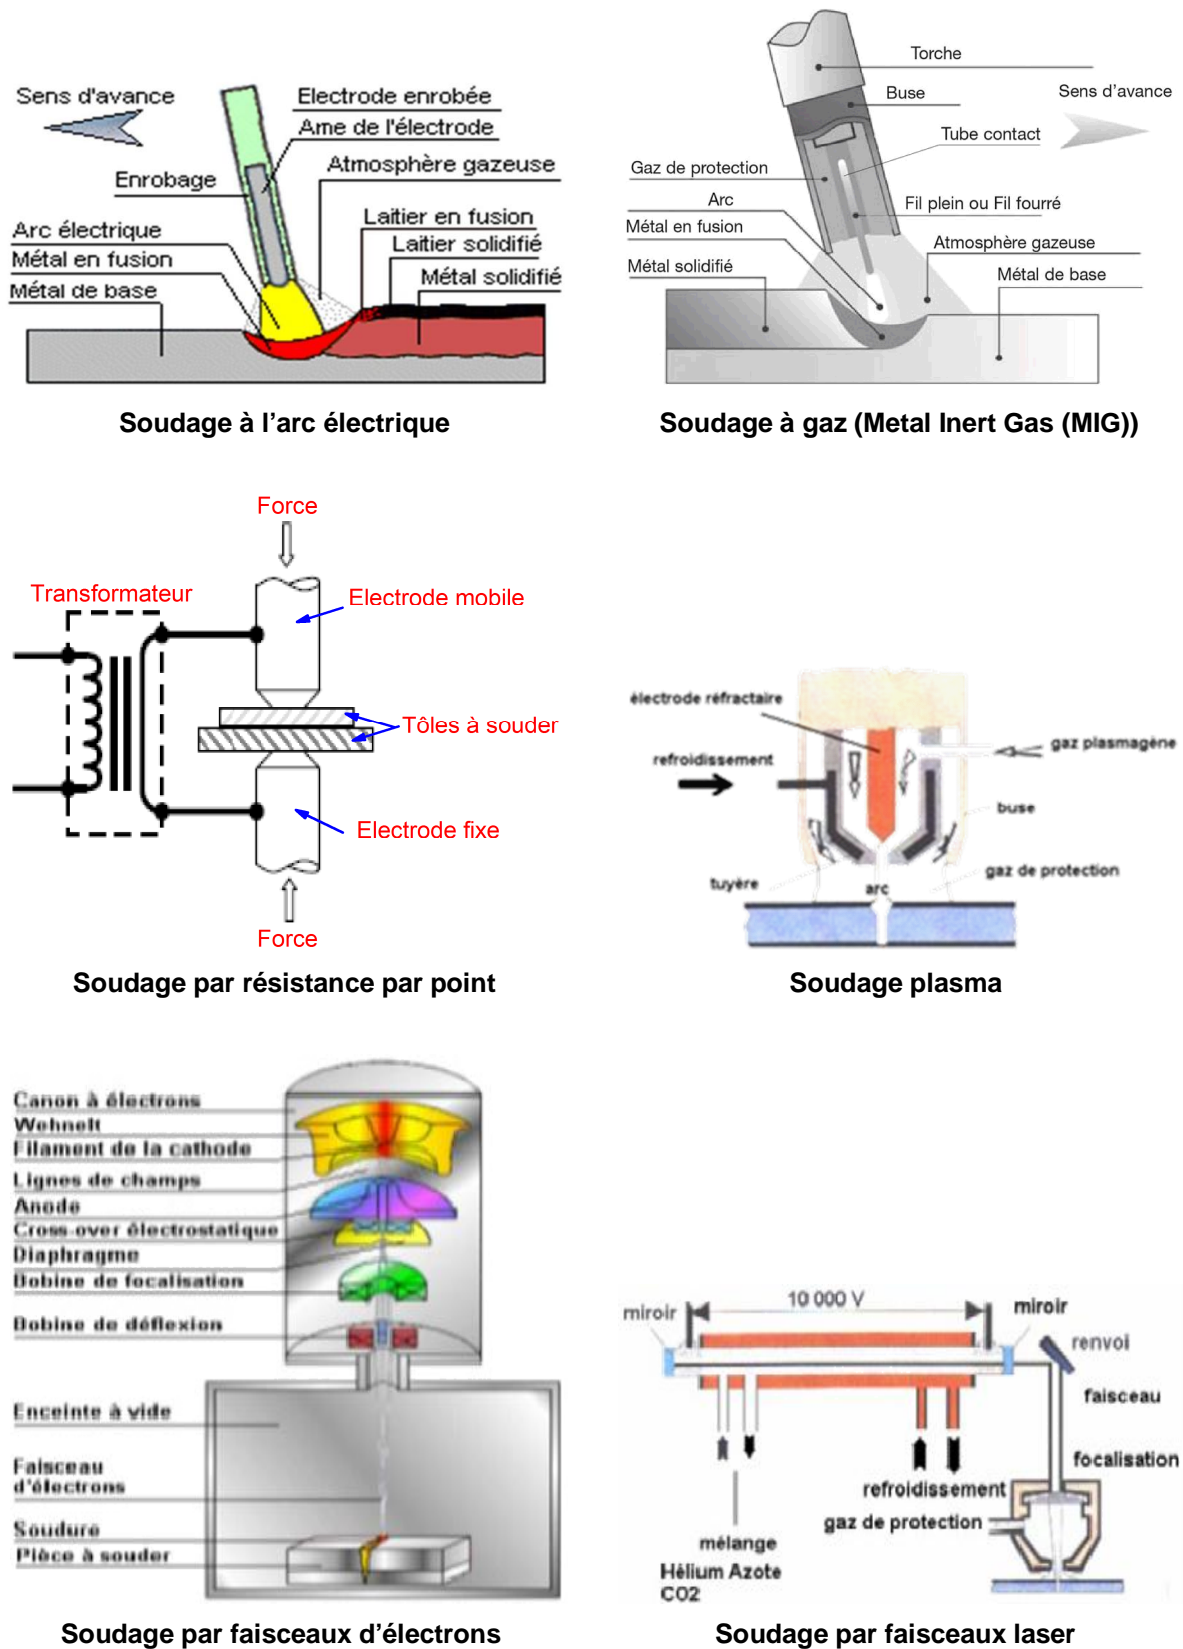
Principaux procédés de soudage avec fusion [2, 3, 4].
